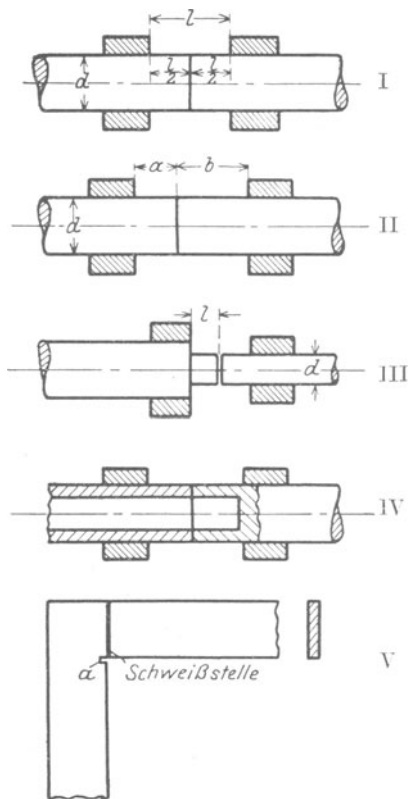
Einspannlängen und Schweißquerschnitte beim Stumpfschweißen.
